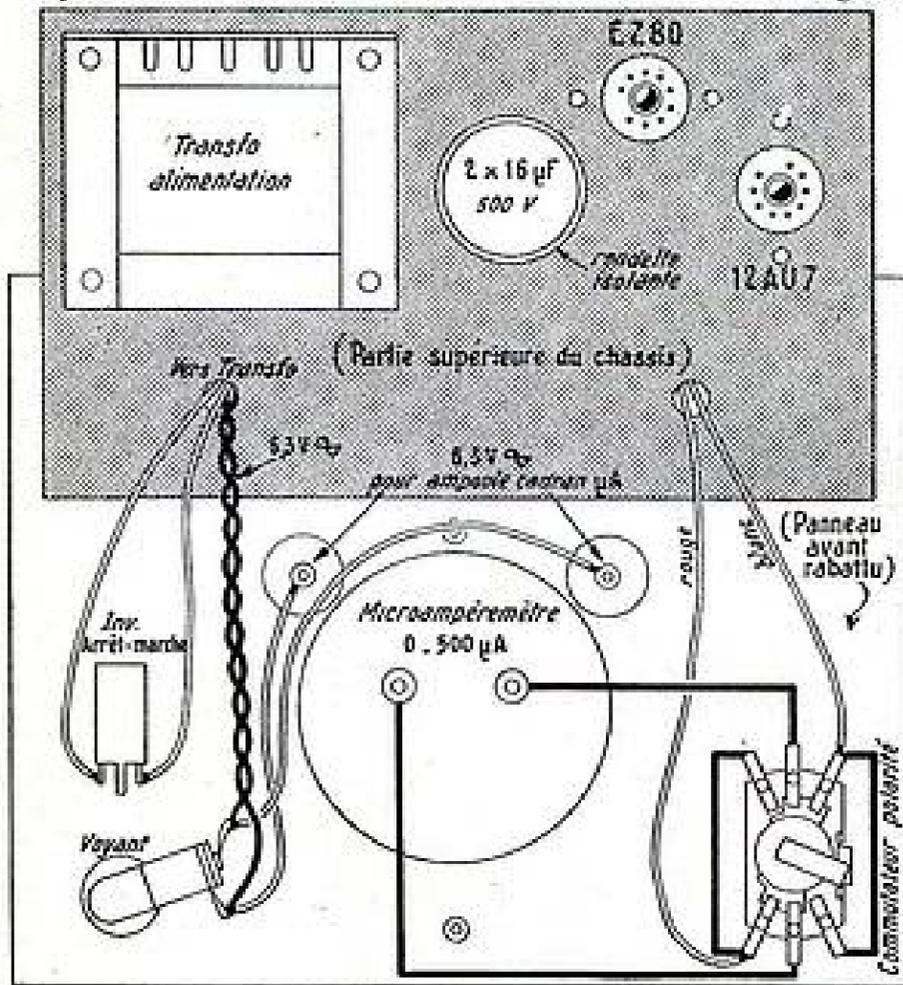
Vue de dessus du châssis et du panneau avant rabattu.
